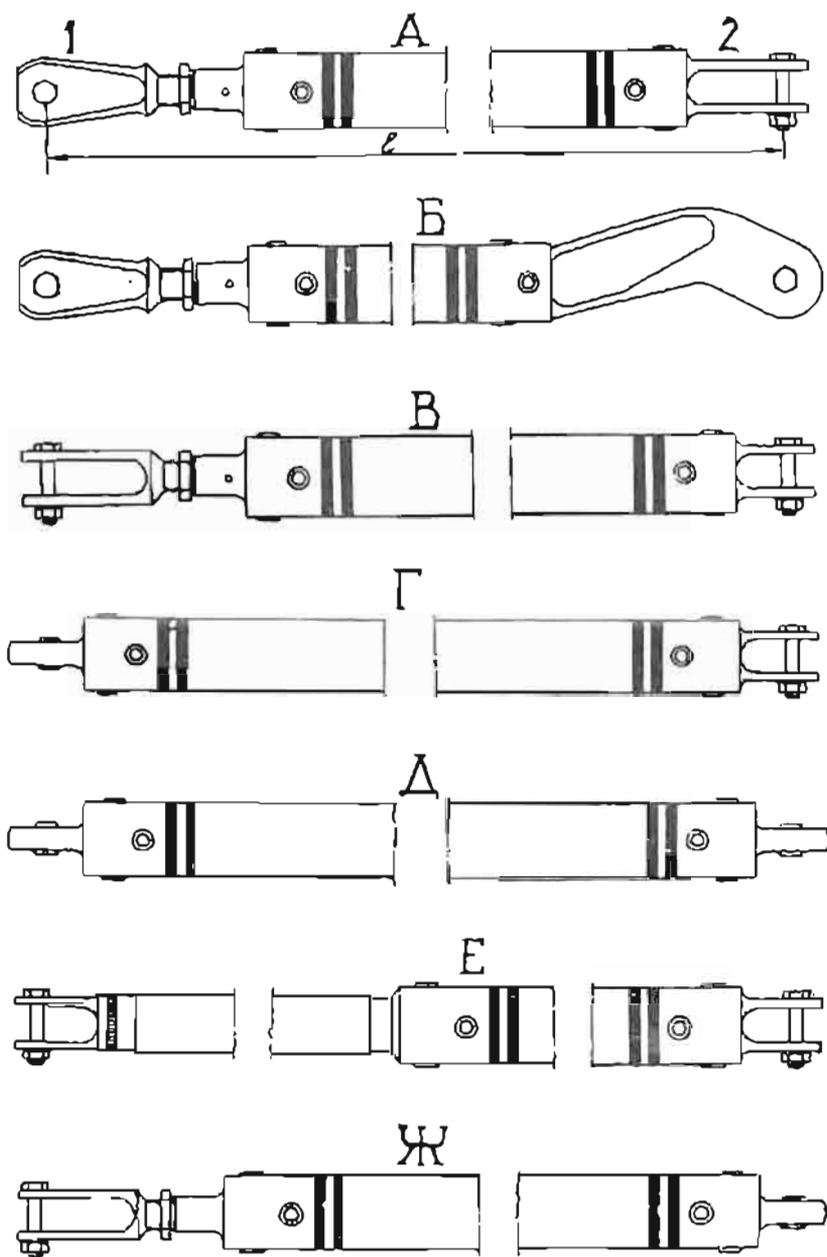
Kennzeichnung der Steueranlagen des Seitenruders
